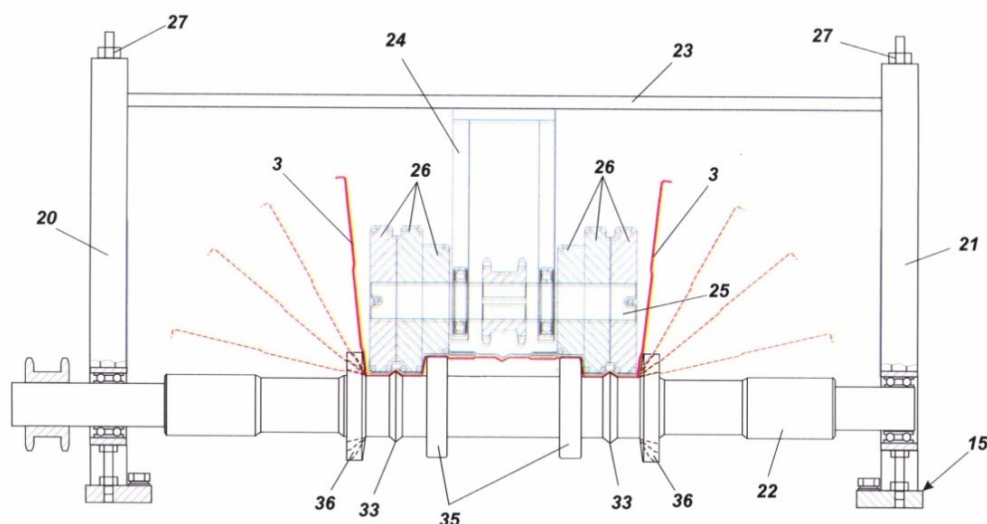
Фрагмент многоклетьевого профилегибочного стана изготовления профиля [5]:
